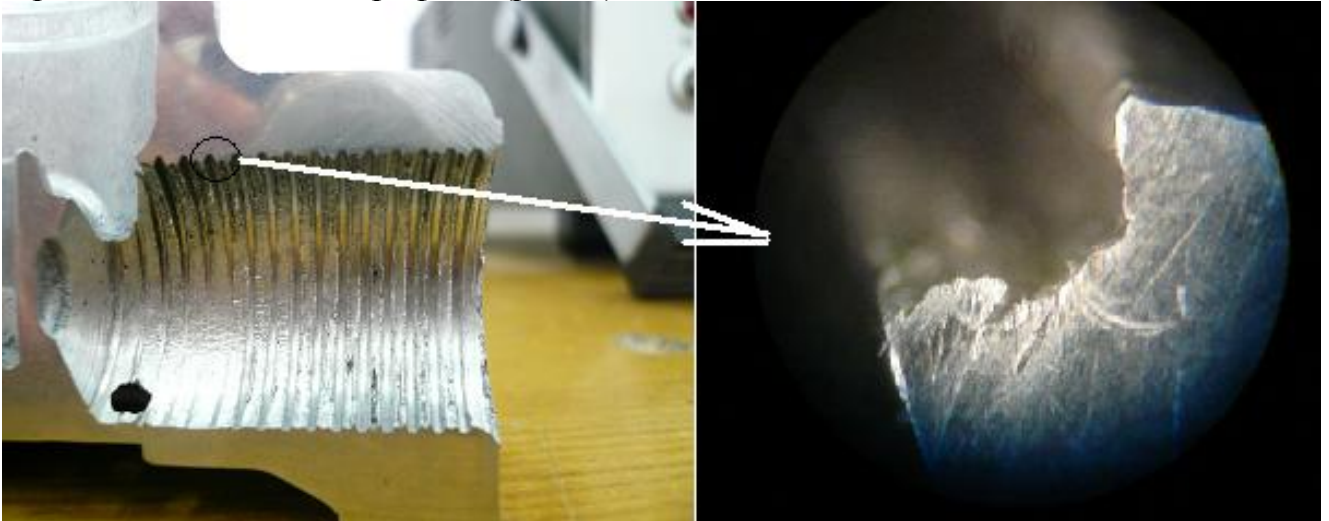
Неповний профіль трубної циліндричної різьби внаслідок неточного розрахунку середнього діаметра під наочення
